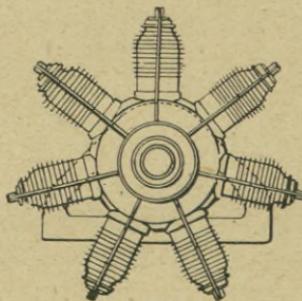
Umlaufmotor mit luftgekühlten Zylindern.
